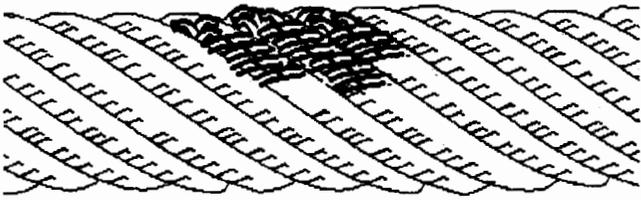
Deterioro avanzado. INACEPTABLE. -
